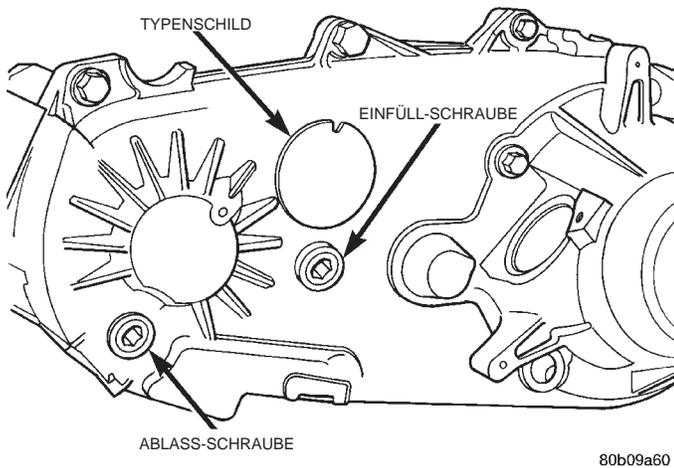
Einfüllschraube, Ablaßschraube und Typenschild
